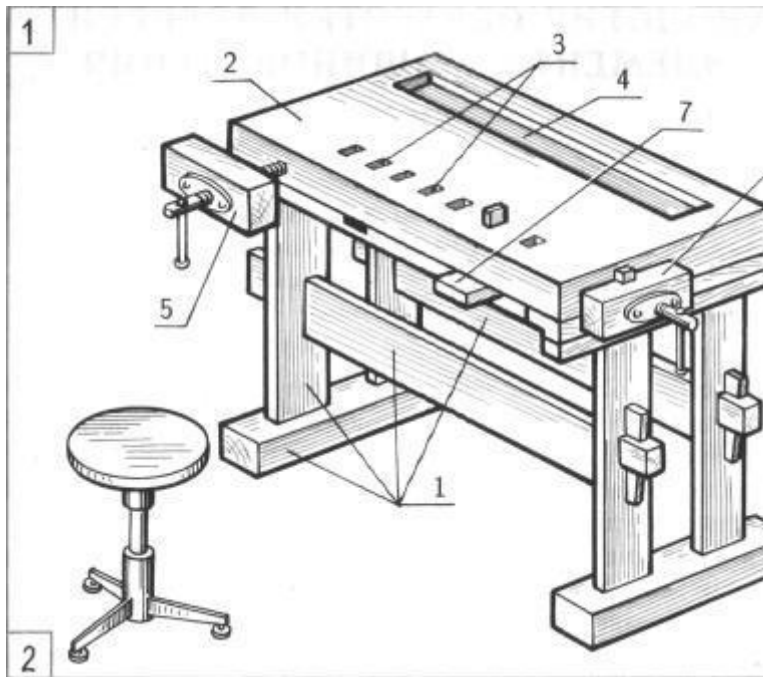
Столярный верстак: 1 — подверстажье; 2 — крышка; 3 — отверстия под клинья; 4 — лоток; 5 — передний зажим; 6 — задний зажим; 7 — выдвижные или поворотные пальцы
